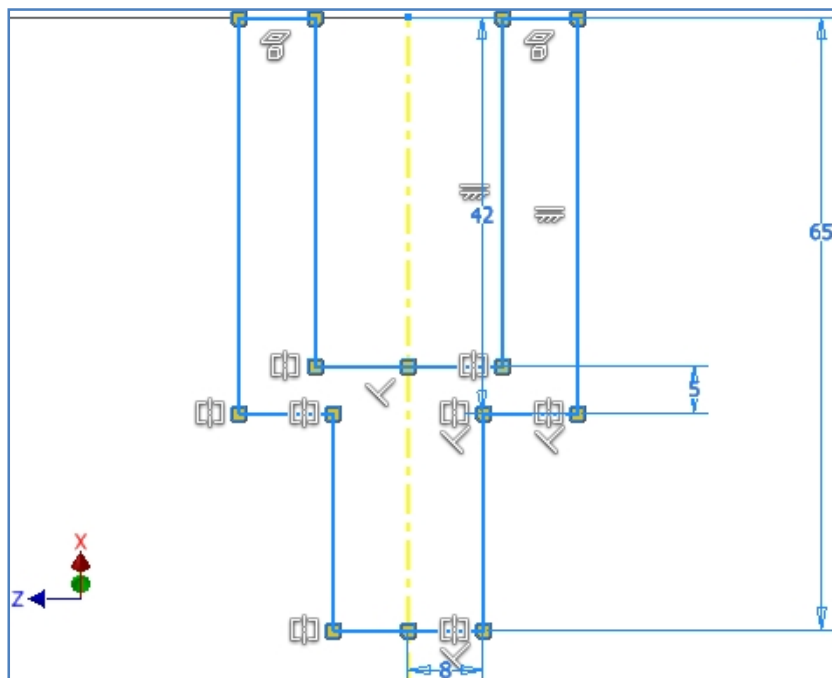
Boceto sobre el plano de trabajo 1 para realizar la primera extrusión.
